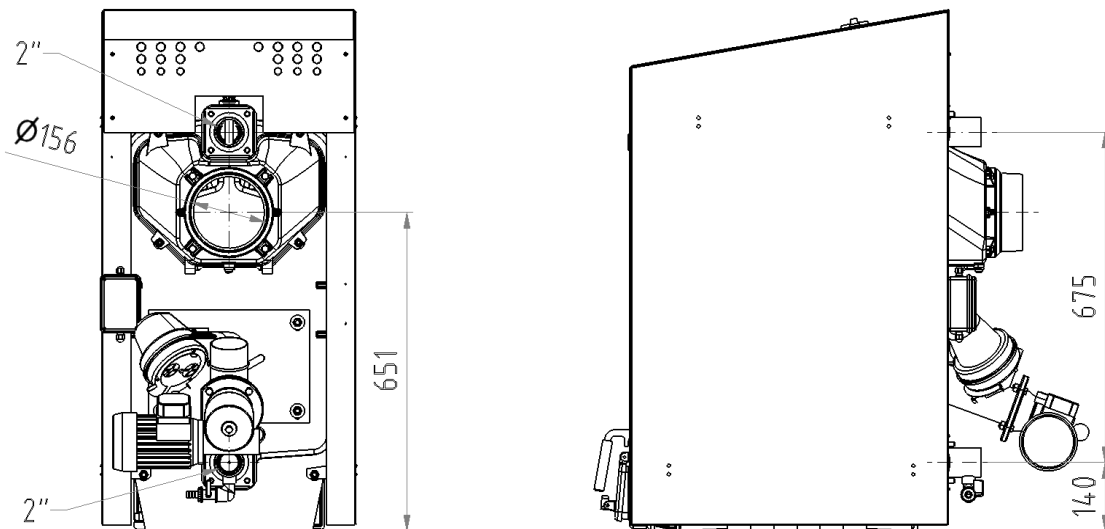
Присоединительные размеры котла VIADRUS HERCULES ECO
